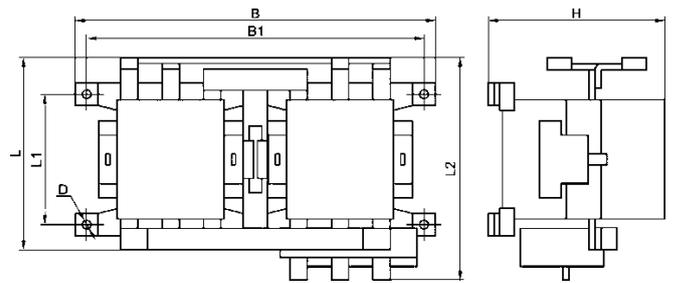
Пускатель реверсивный ПМ12 100-250А. Степень защиты - IP00
